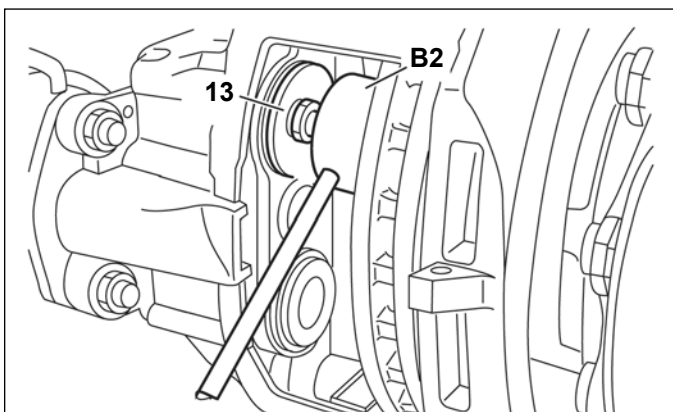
INSTALLATION DU POUSSOIR SUR LE VÉHICULE
